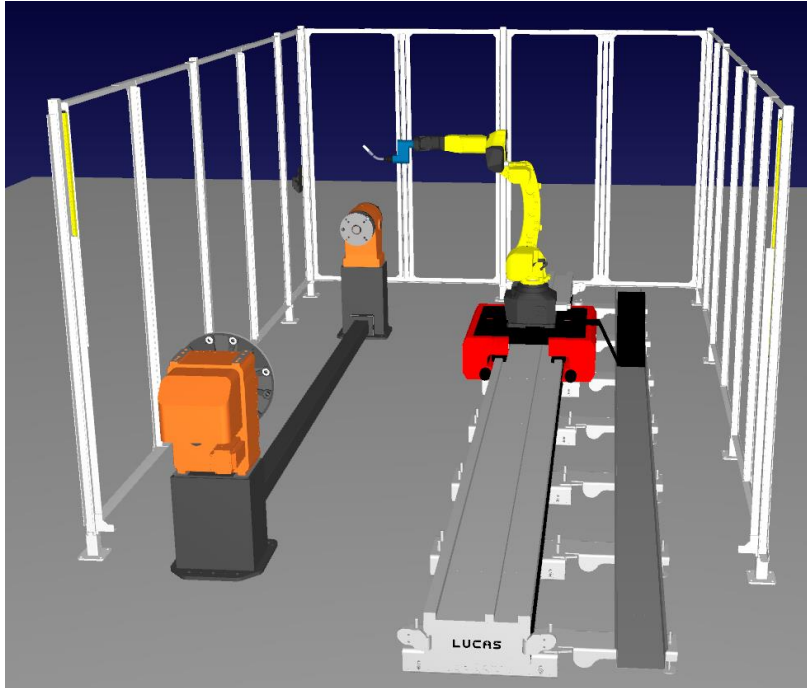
Idealização de uma célula de soldadura de um robô convencional com uma guia de translação e um posicionador rotativo
